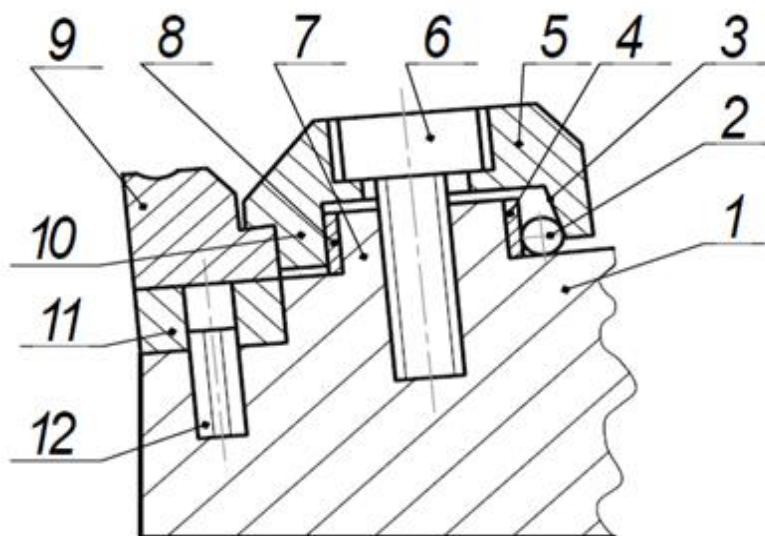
Сборный резец по авторскому свидетельству №1232384 (конструкция 4)
